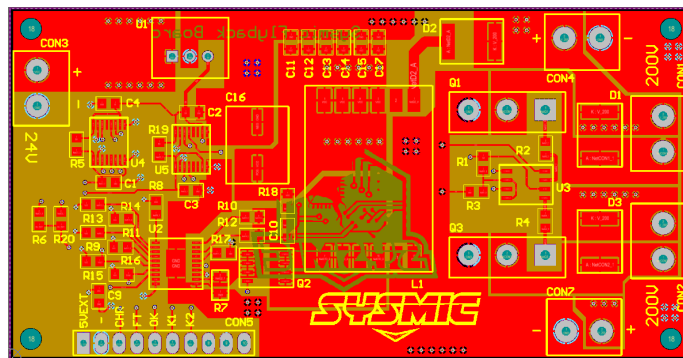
Diseño PCB flyback en software Altium Designer.
